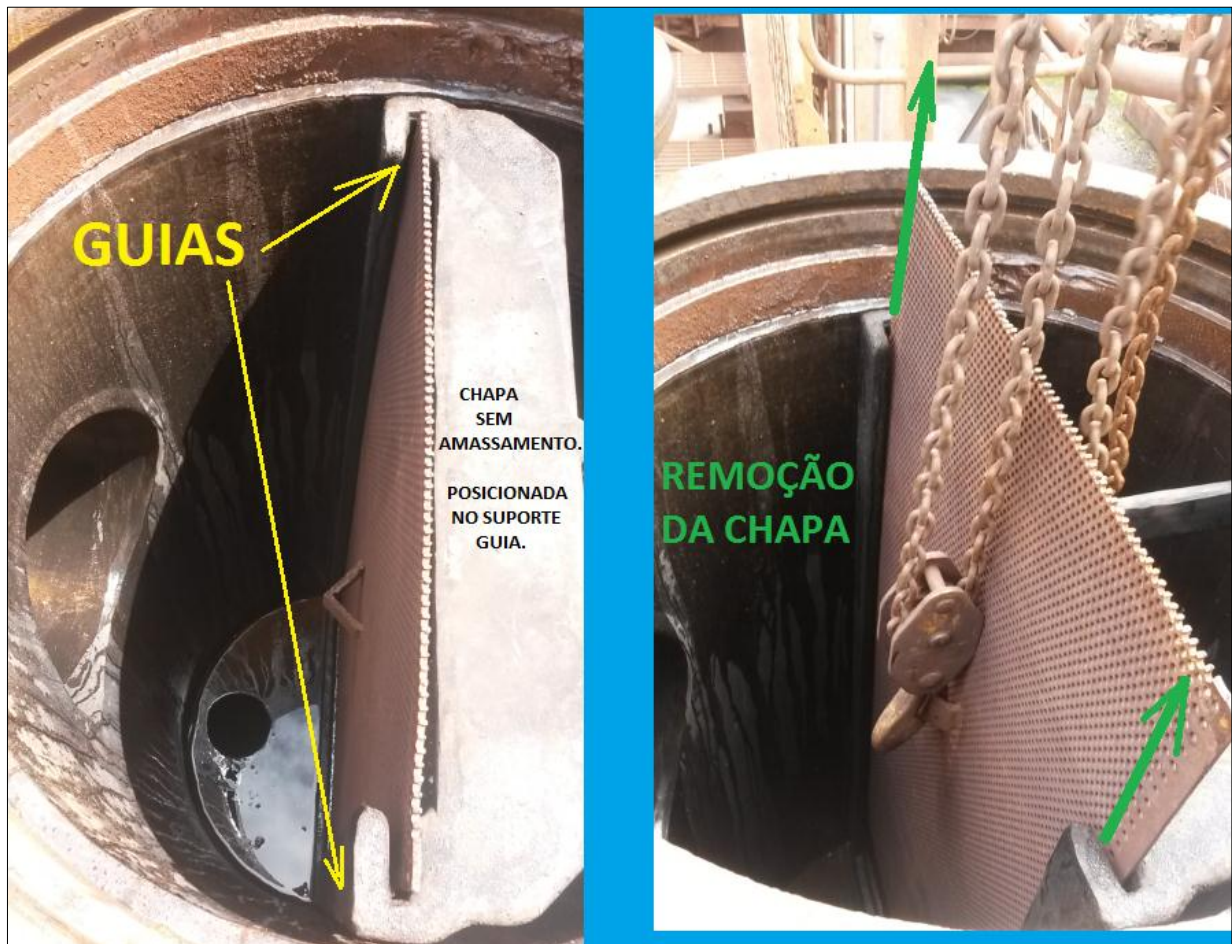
Montagem local da chapa perfurada e detalhe para remoção da mesma
